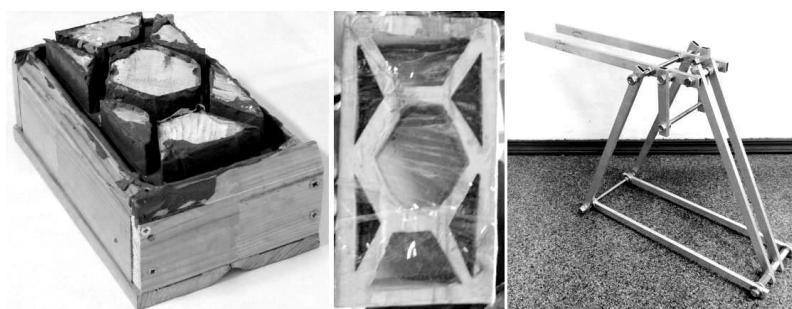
Новый блок-кирпич, форма и пресс для его изготовления
